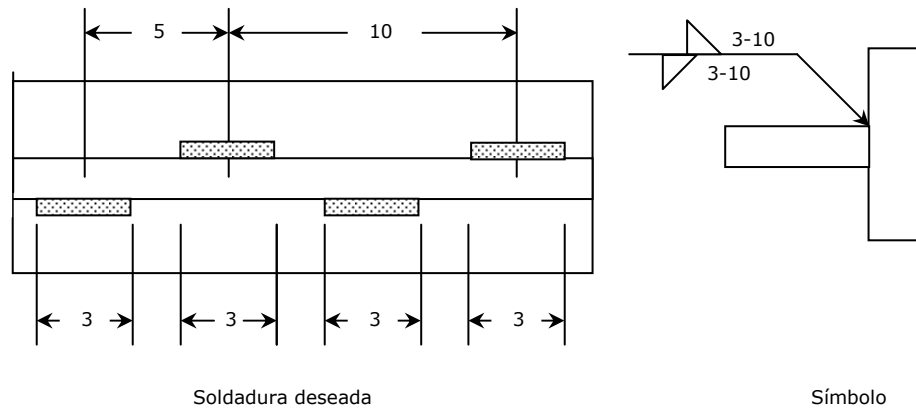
Símbolo de soldadura intermitente y alternada para ambos lados de la unión
